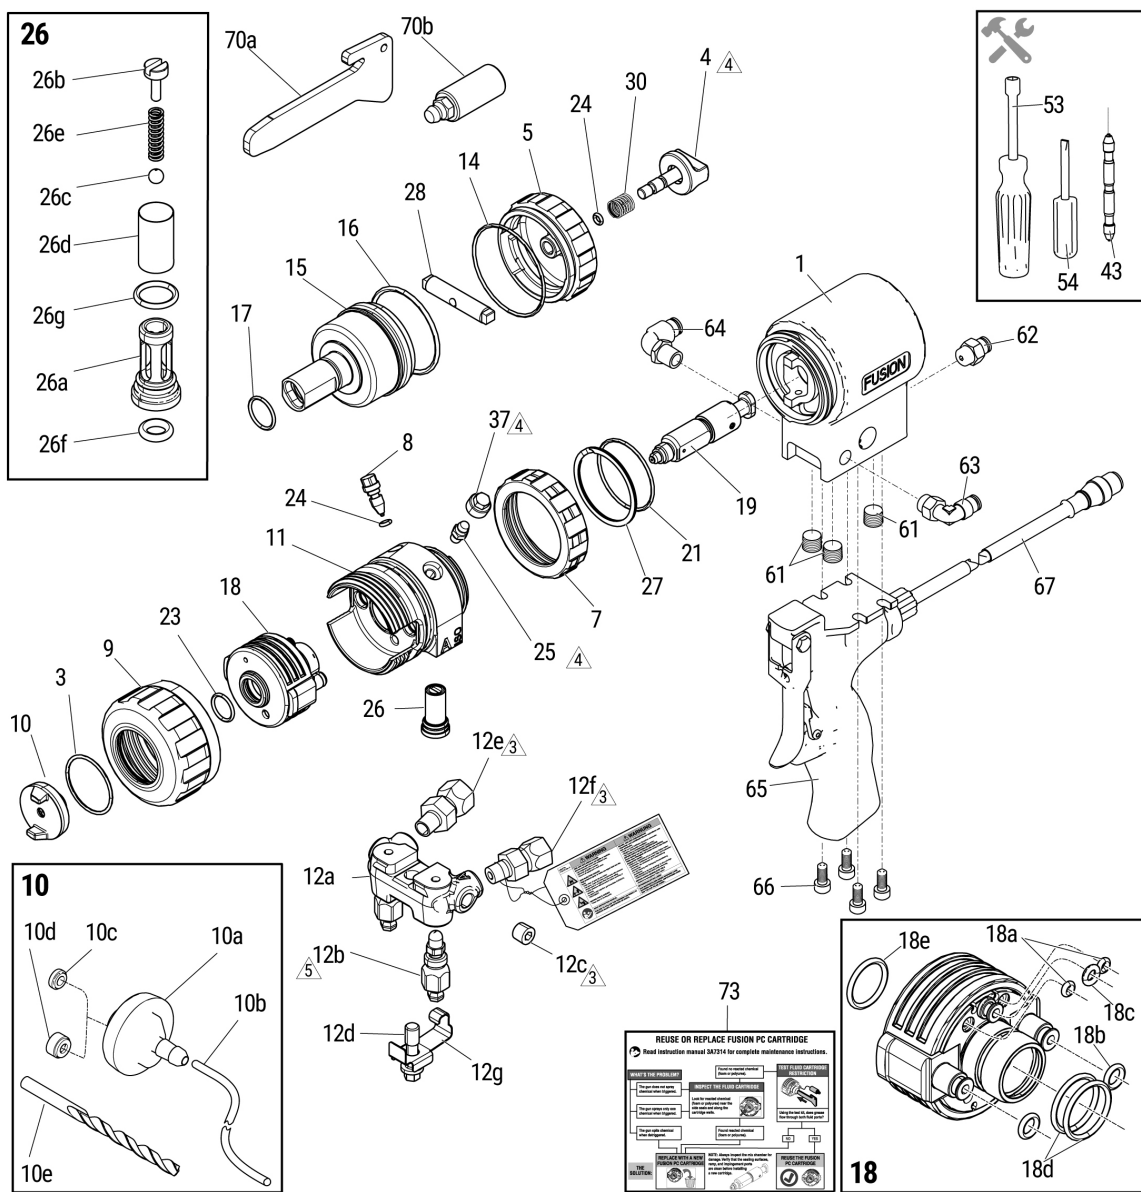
Schema delle parti della pistola a spruzzo Fusion Auto PC a spruzzo pneumatico
